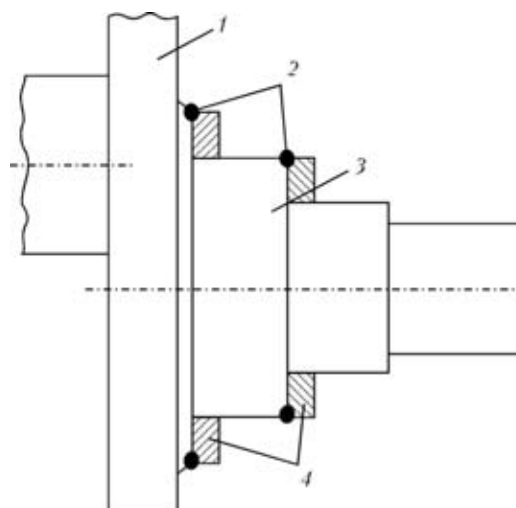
Схема установки ремонтных колец на первой коренной шейке для устранения укорочения наплавленного коленчатого вала: 1 — шейка; 2 — прихватки; 3 — первая коренная шейка; 4 — ремонтные кольца
